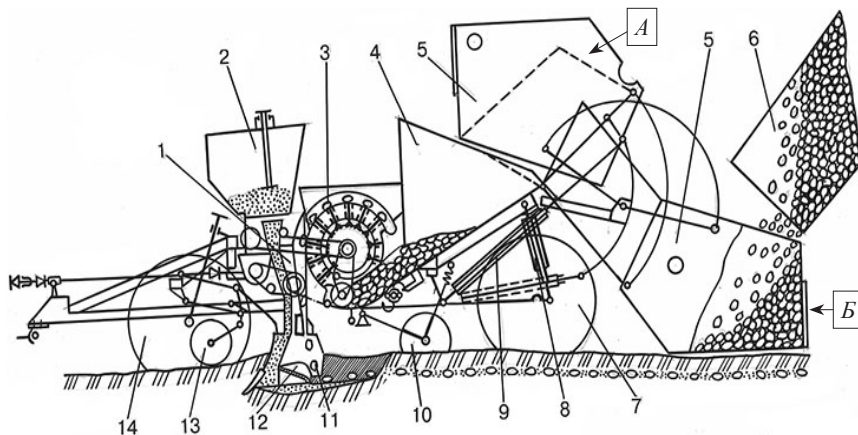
Схема технологического процесса картофелесажалки с дисково-ложечными высаживающими аппаратами: 1 – лоток; 2 – туковысевающий аппарат; 3 – высаживающий аппарат; 4 – рабочий бункер; 5 – загрузочный бункер; 6 – кузов самосвала; 7, 14 – опорные колеса; 8, 9 – гидроцилиндры; 10 – бороздозакрывающие диски; 11 – сошник; 12 – отвальчик; 13 – опорно-копирующее колесо; А – положение загрузочного бункера при посадке; Б – положение загрузочного бункера при заполнении
